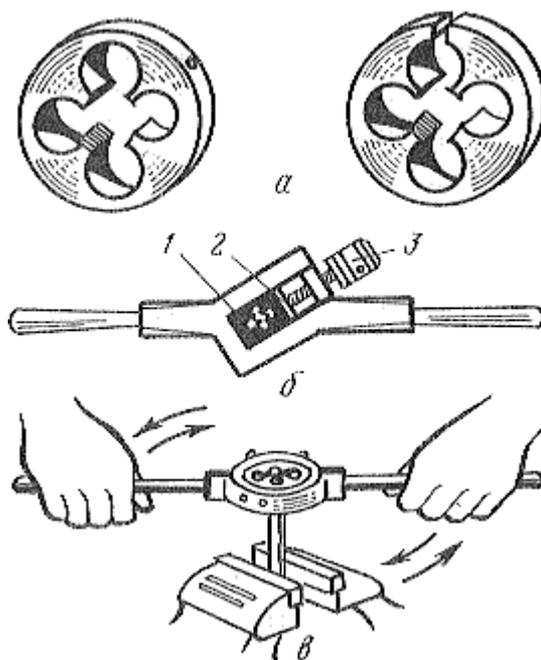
Нарезание наружной резьбы: а - круглая плашка, б - призматическая (раздвижная) плашка, в - нарезание резьбы
